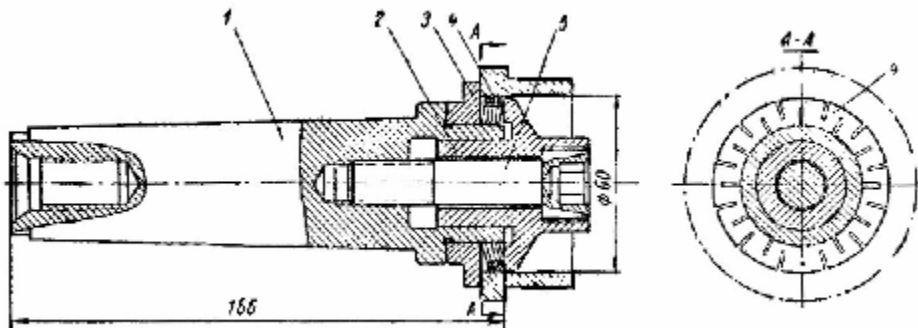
Консольная оправка с тарельчатыми пружинами
